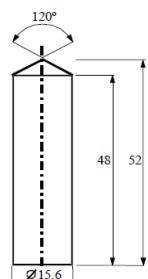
Pistón cilíndrico de bronce, dimensiones en mm.
